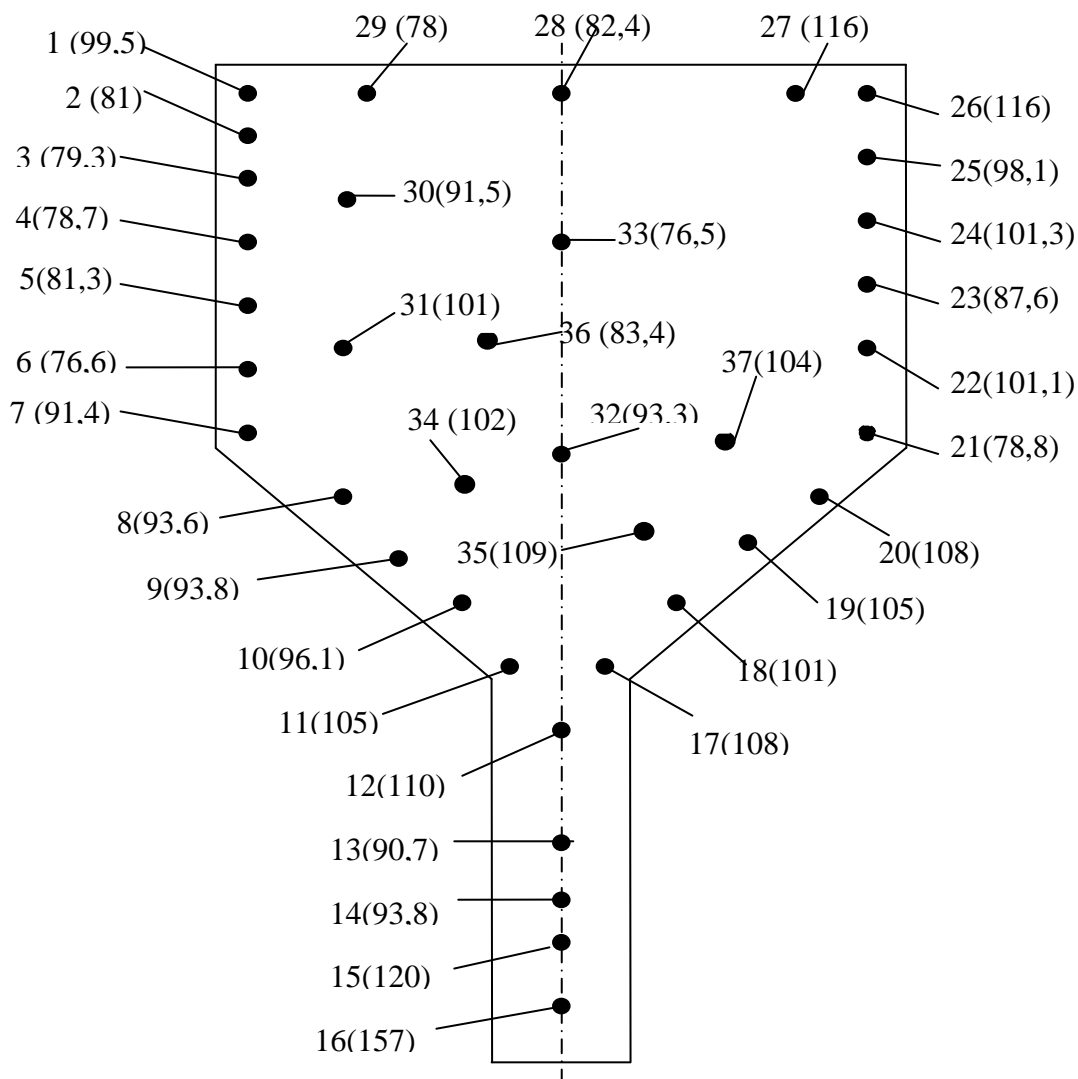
Схема недопрессованной заготовки из смеси стружки меди и латуни Л63 с указанием мест замеров значений твердости по Бринеллю
